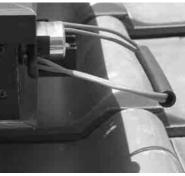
Glissez l'outil de desserrage derrière le raccord à collerette
